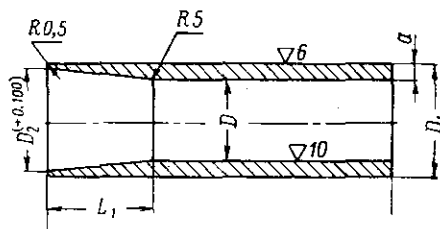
Типовая конструкция конусной втулки для механического осаживания защитных фторопластовых шайб
